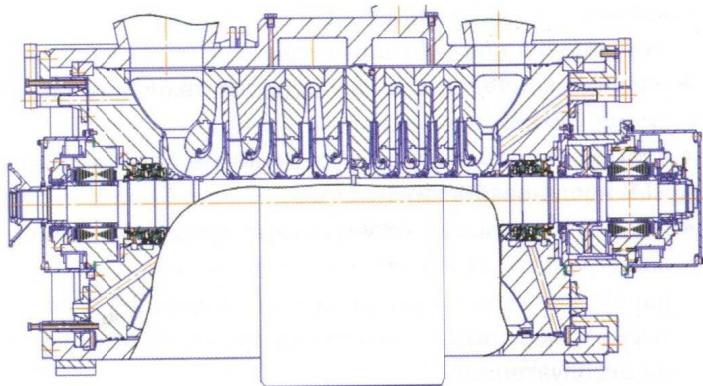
Компрессор 5ГЦ2-300/4,5-64
